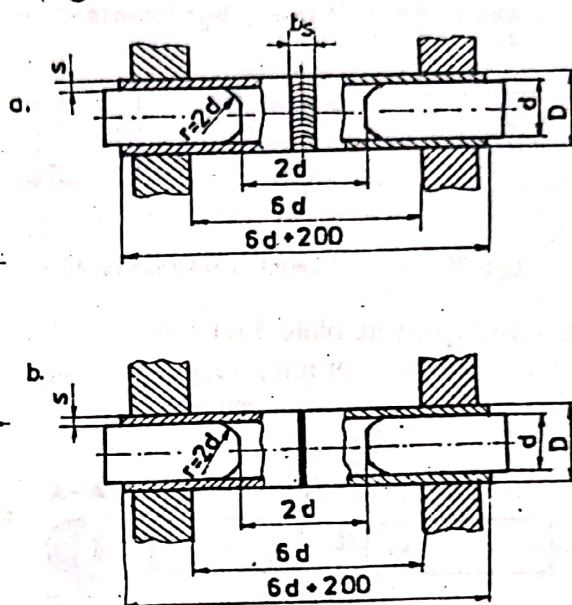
Epruvete tronson-tubulare din țevi cu $D \leq 51\text{ mm}$: a-sudare prin topire; b-sudare prin presiune.
